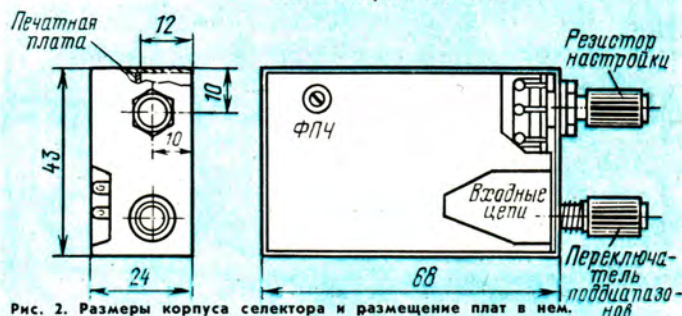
Размеры корпуса селектора и размещение плат в нем.
